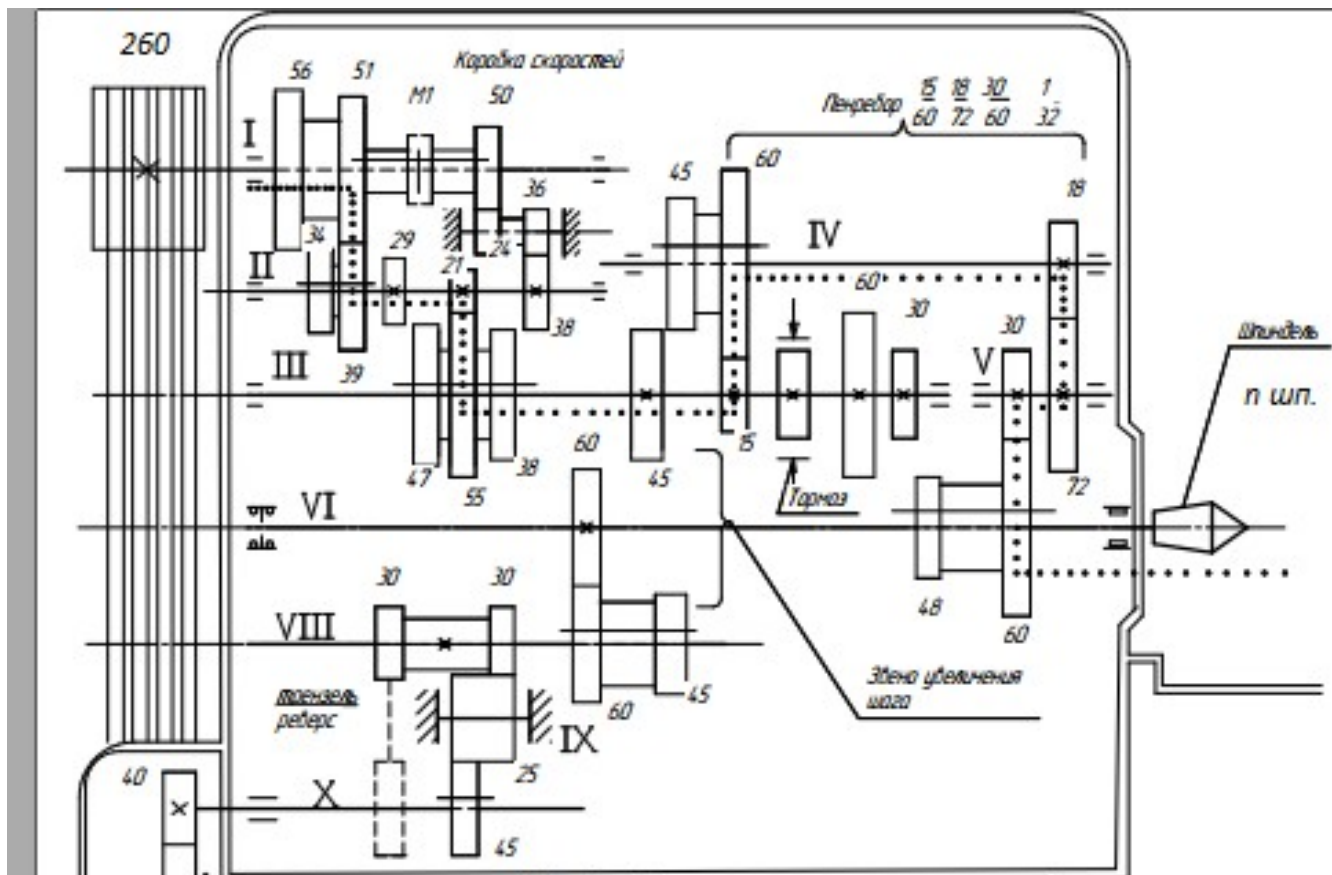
Фрагмент кинематической схемы токарно-винторезного станка модели 16K20
